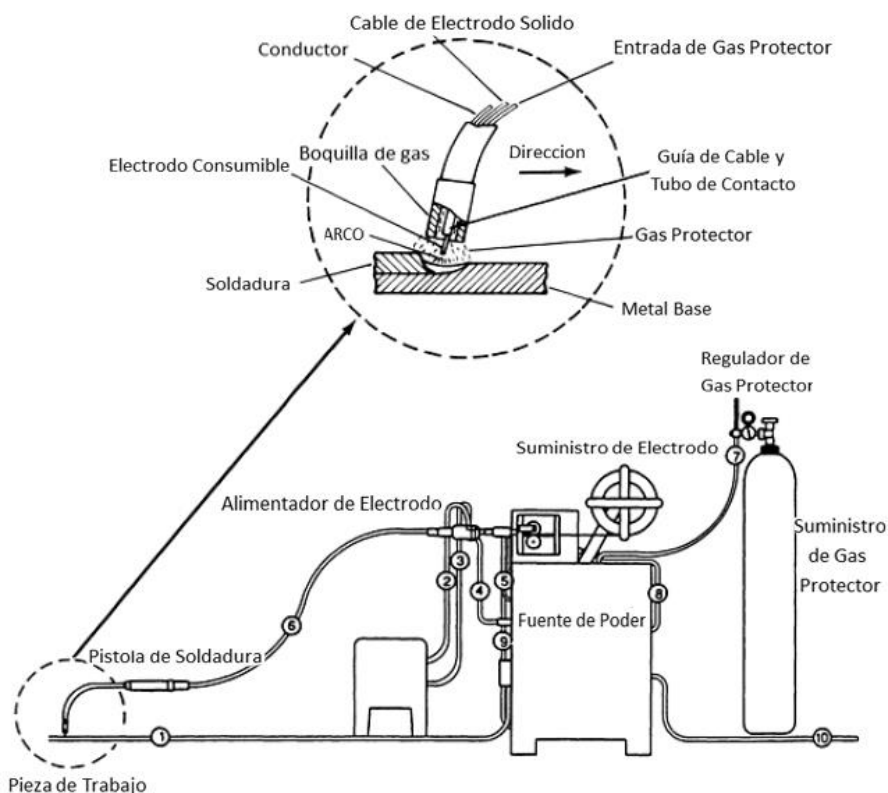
Esquema de Proceso de Soldadura GMAW [4].
